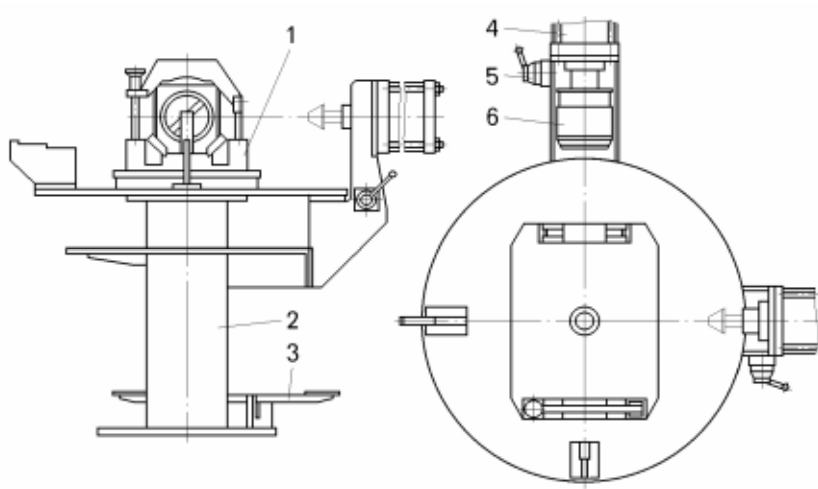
Стенд для сборки цилиндров опрокидывающего механизма СБ-61:
